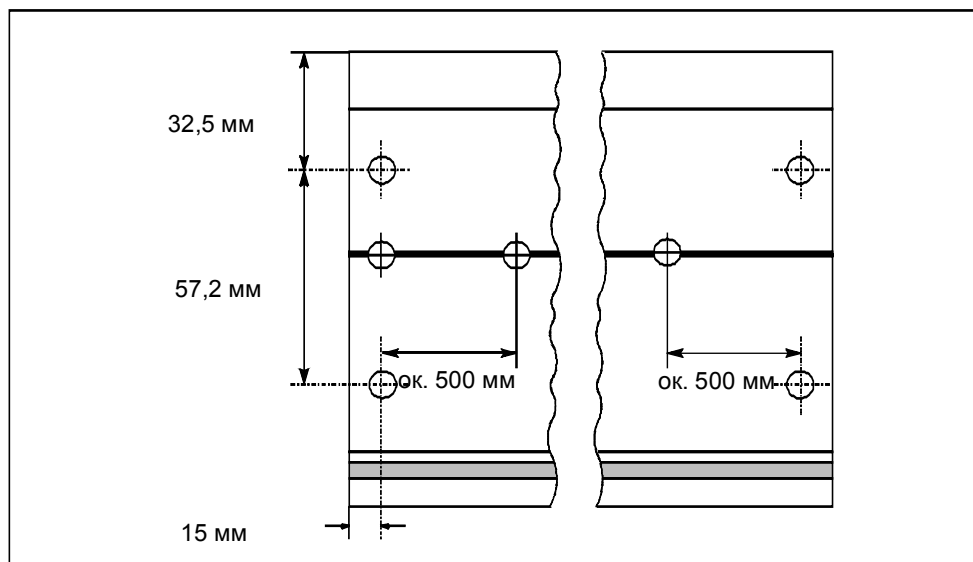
Размеры для крепежных отверстий у 2-метровой профильной шины
